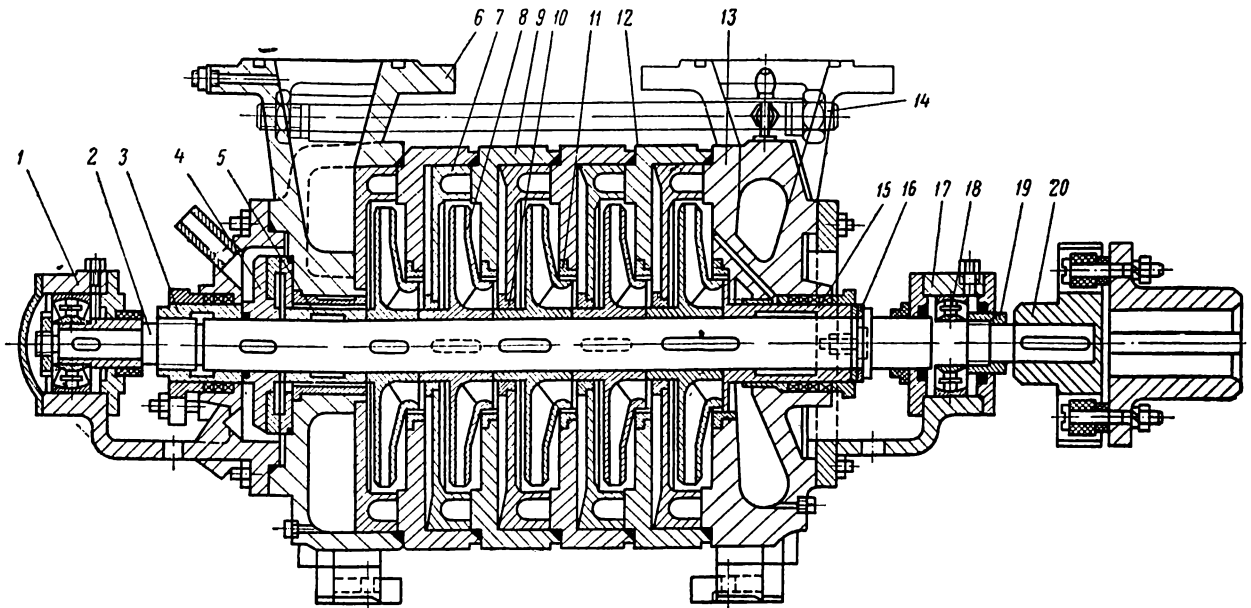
Насосы ЦНС 180-85...425 и ЦНС 300-120...600
